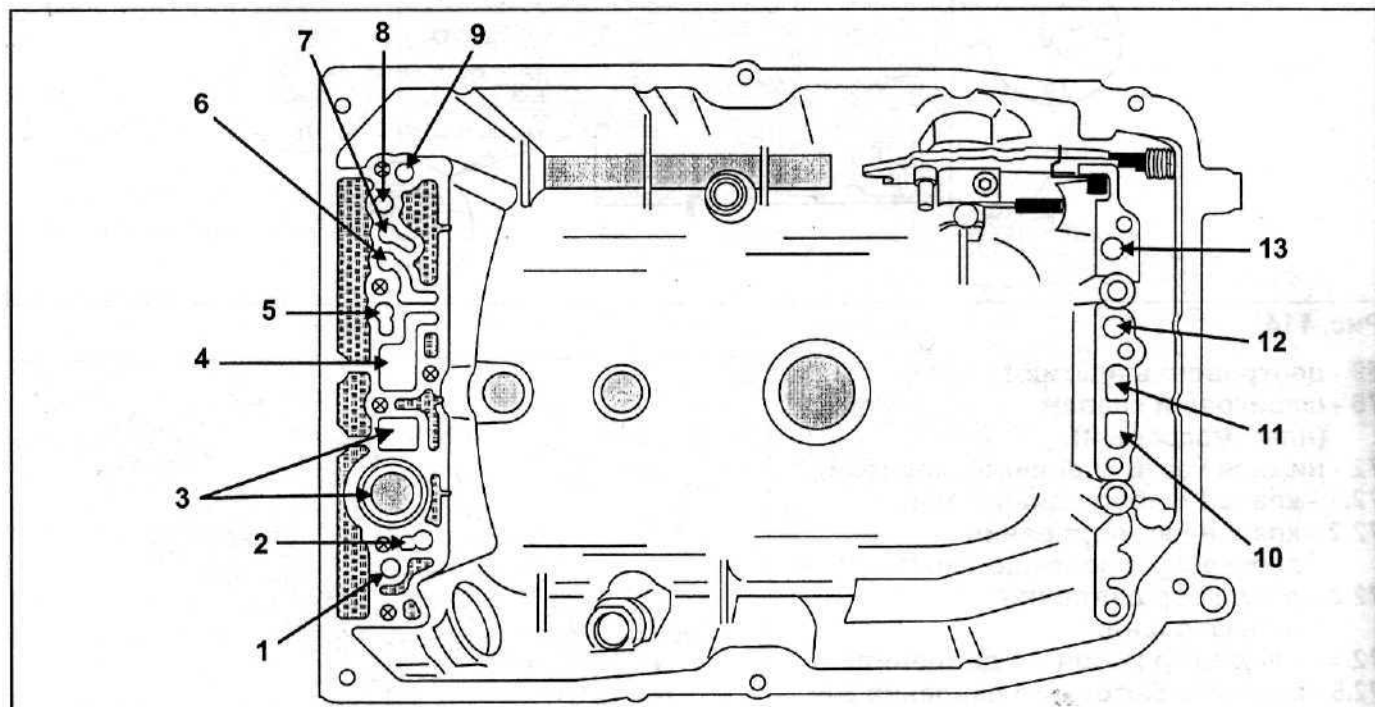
Назначение отверстий в картере коробки передач (со стороны клапанной коробки).
